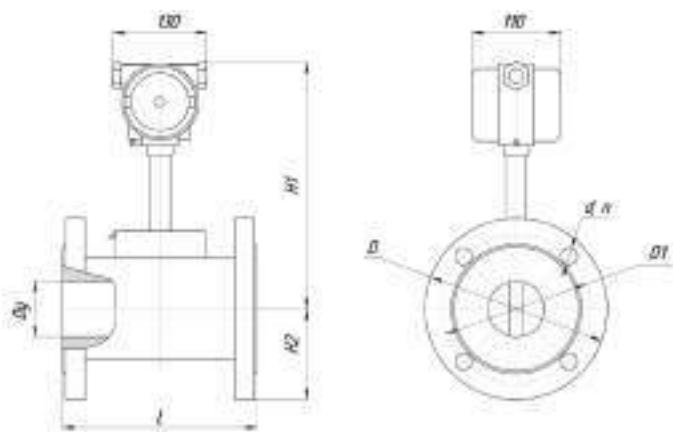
Габаритные и присоединительные размеры для преобразователя Тирэс фланцевого конструктива (исполнение А) температурного исполнения Т1.
